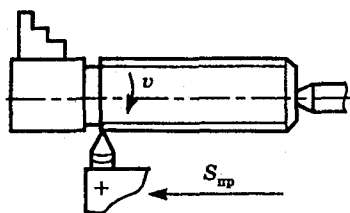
Схема нарезания однозаходной резьбы на токарно-винторезном станке
